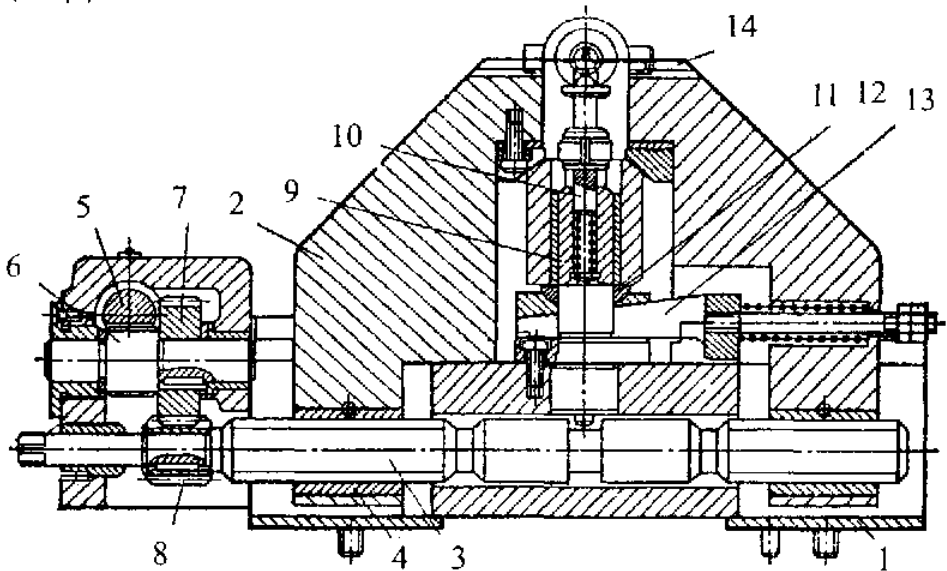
Схема пристрою-супутника для встановлення вилки і хрестовини кардана: 1 – основа; 2 – повзуни з призми 14; 3 – гвинт; 4 – гайка; 5 – рейка; 6, 7, 8 – шестерні; 9 – оправка; 10 – орієнтач; 11, 12 – кулькова опора; 13 – клин.
